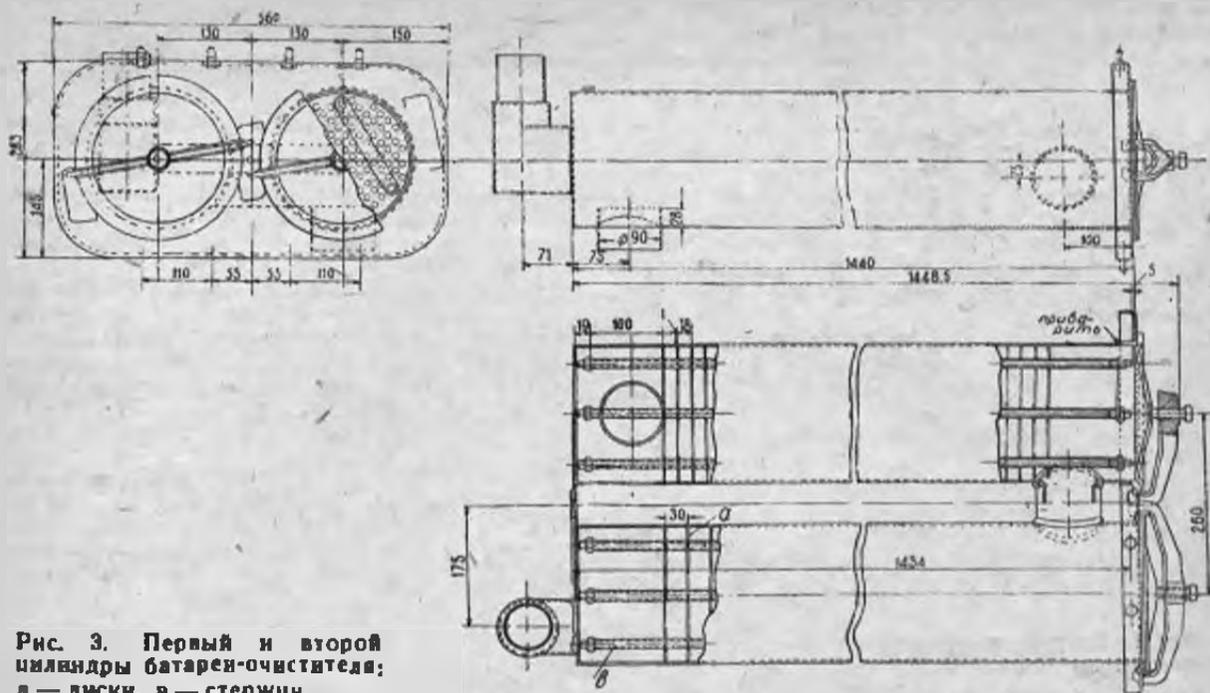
Первый и второй цилиндры батарей-очистителя; а — диски, б — стержни
